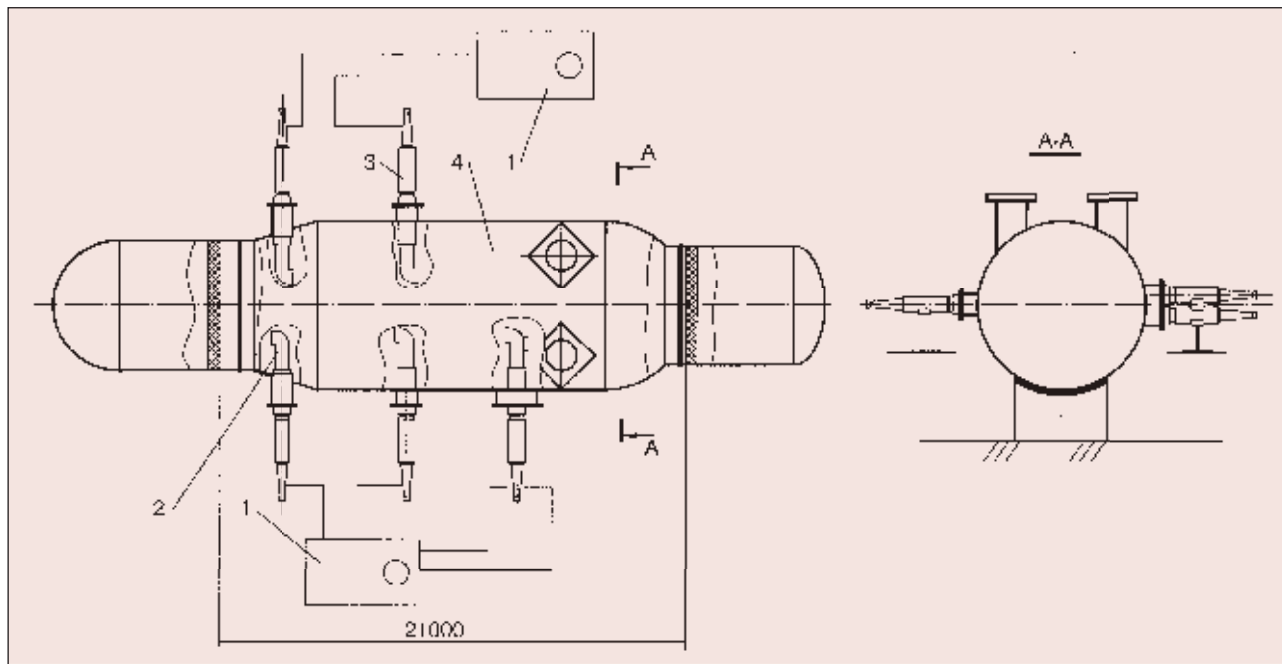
Схема термообработки участка корпуса: 1 — топливные емкости; 2 — устройства ввода теплоносителя; 3 — теплогенераторы; 4 — участок корпуса
